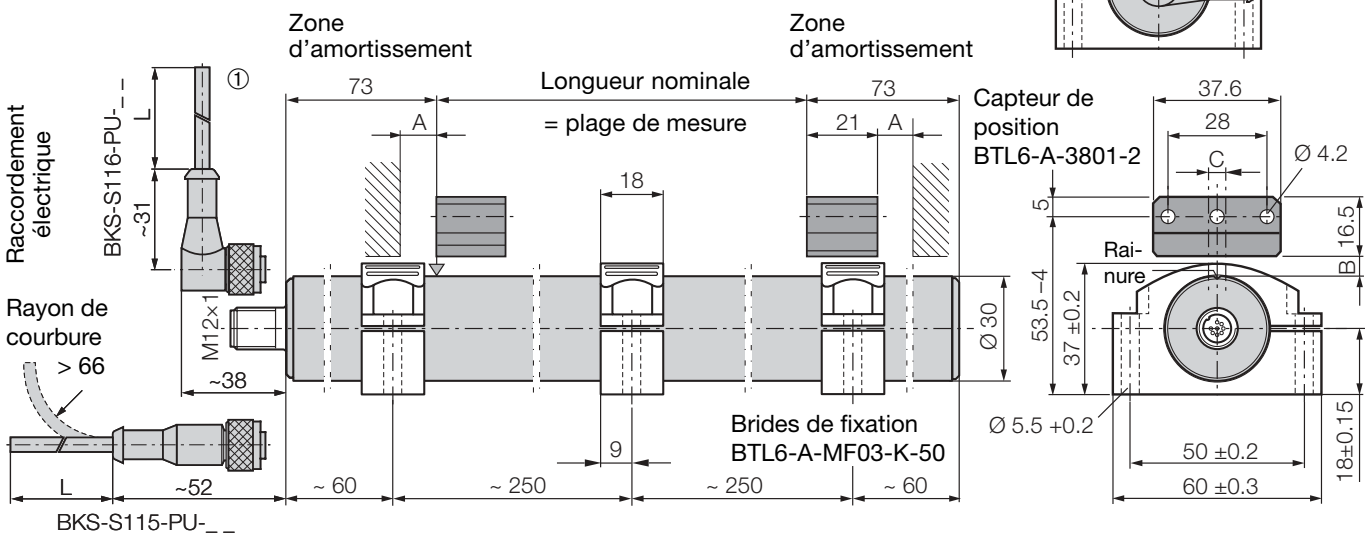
Plan coté (capteur de déplacement BTL6...A1-S115 avec capteur de position BTL6-A-3801-2 et brides de fixation BTL6-A-MF03-K-50)
